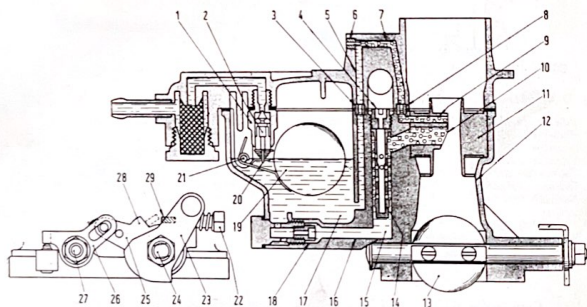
Carburador Bressel-Weber 30 DIC 1.
